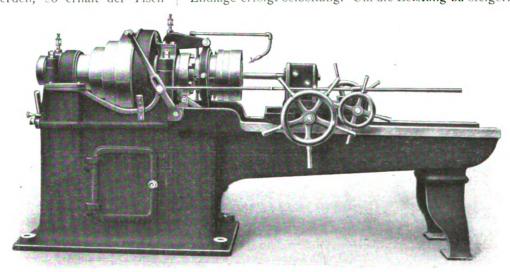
Schraubenschneidmaschine für Kupplungsschrauben von Carl Klingelböffer G. m. b. H.. Erkelenz (Rheinland).
